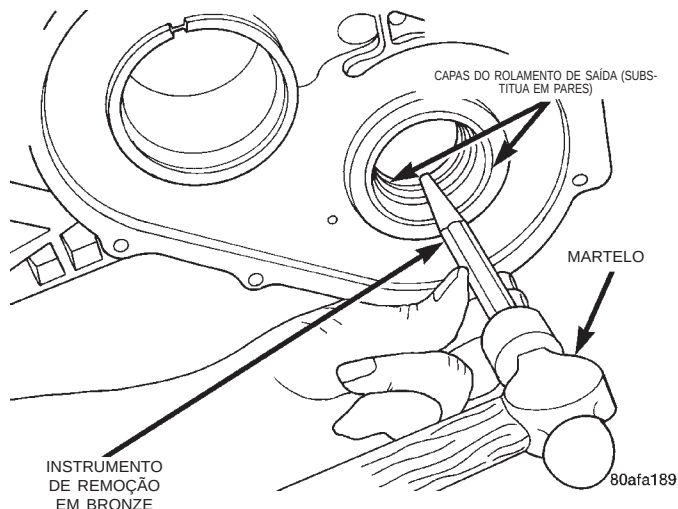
Remoção da Capa Interna do Rolamento de Saída
